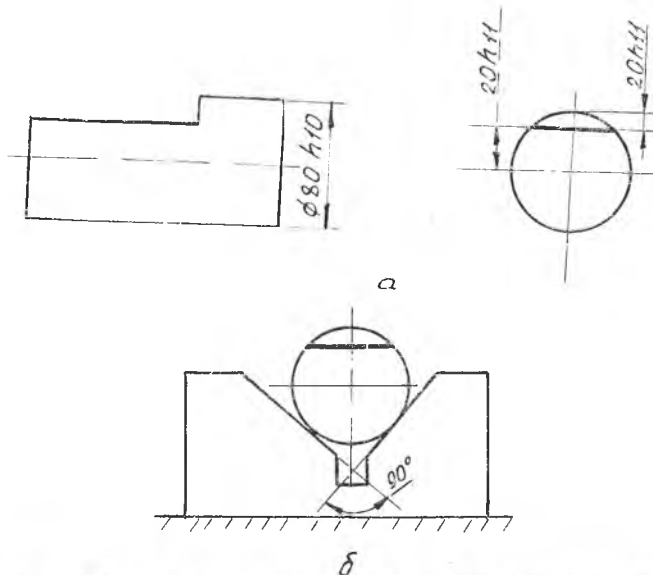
К расчету точности обработки при фрезеровании с установкой в призму: а — операционный эскиз; б — приспособление
